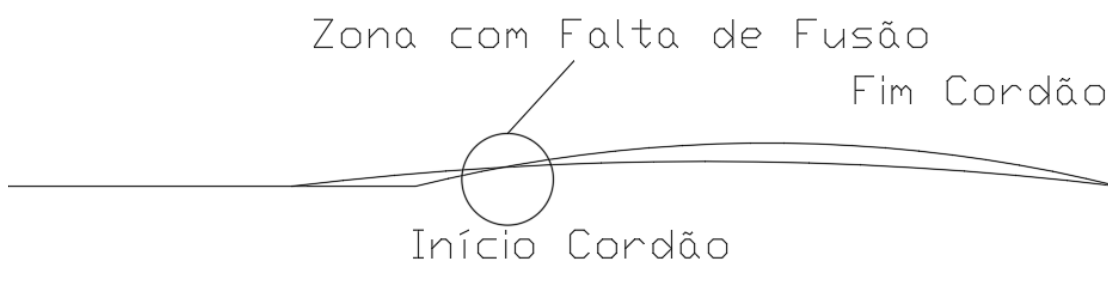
Sobreposição do Cordão de Soldadura Circunferencial
